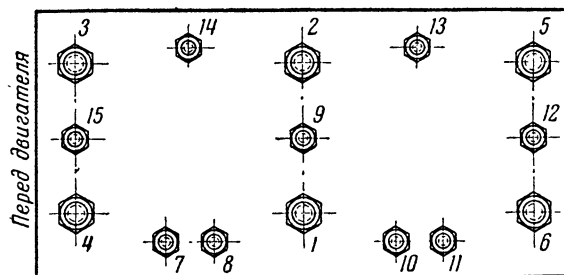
Схема затяжки гаек шпилек крепления головки цилиндров.
